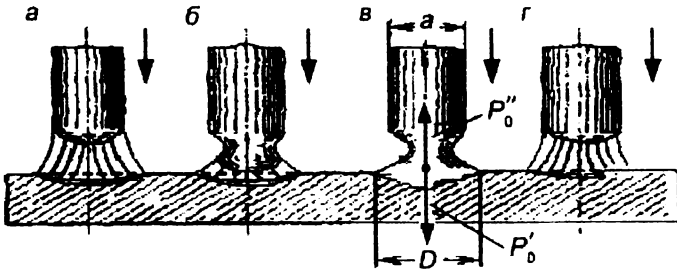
Схема переноса электродного металла через дугу при сварке короткой дугой
